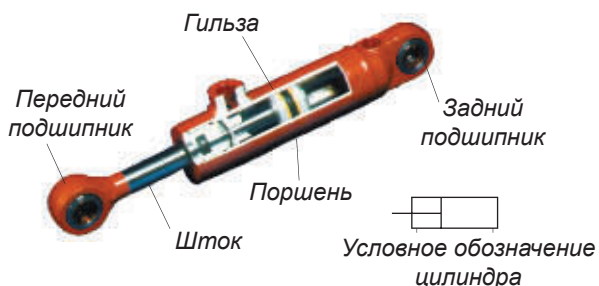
Гидроцилиндр двойного действия (с вырезом)
